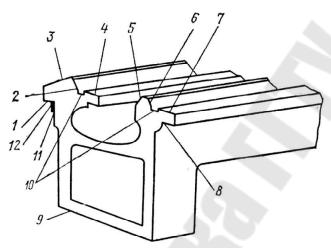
Направляющие станины токарно-винторезного станка модели 1A62
